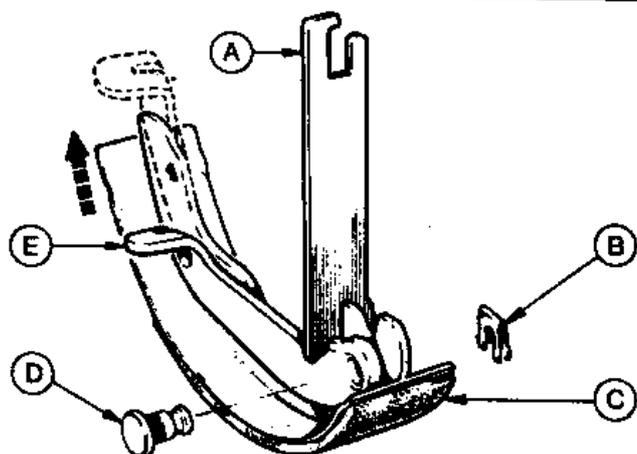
Рычаг привода ручного тормоза (А), клипс (В), тормозная колодка (С), шарнирный палец (D) и распорка (Е) (Разд.8)
